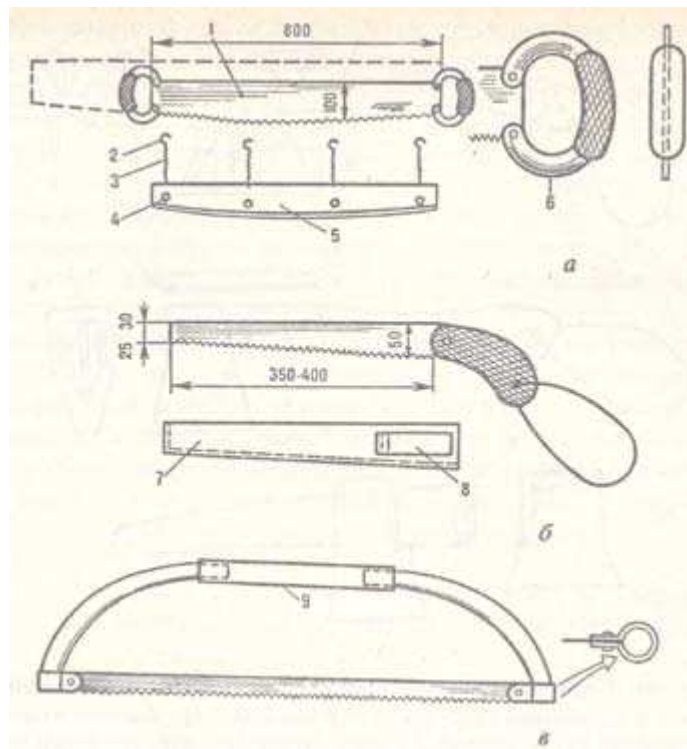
Походные пилы: а — укороченная двуручная; б — ножовка; в — лучковая, 1 — уменьшенное полотно большой пилы; 2 — крючки; 3 — резинки; 4 — петли; 5 — чехол; 6 — овальные ручки; 7 — чехол для ножовки; 8 — петля для ремня; 9 — дюралевые трубки.
